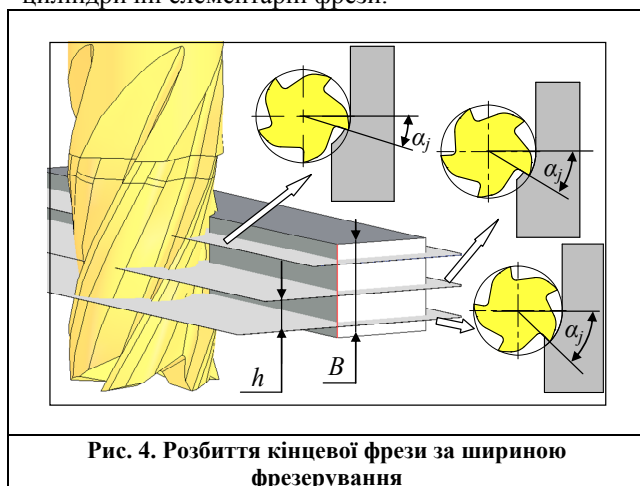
Розбиття кінцевої фрези за шириною фрезерування
